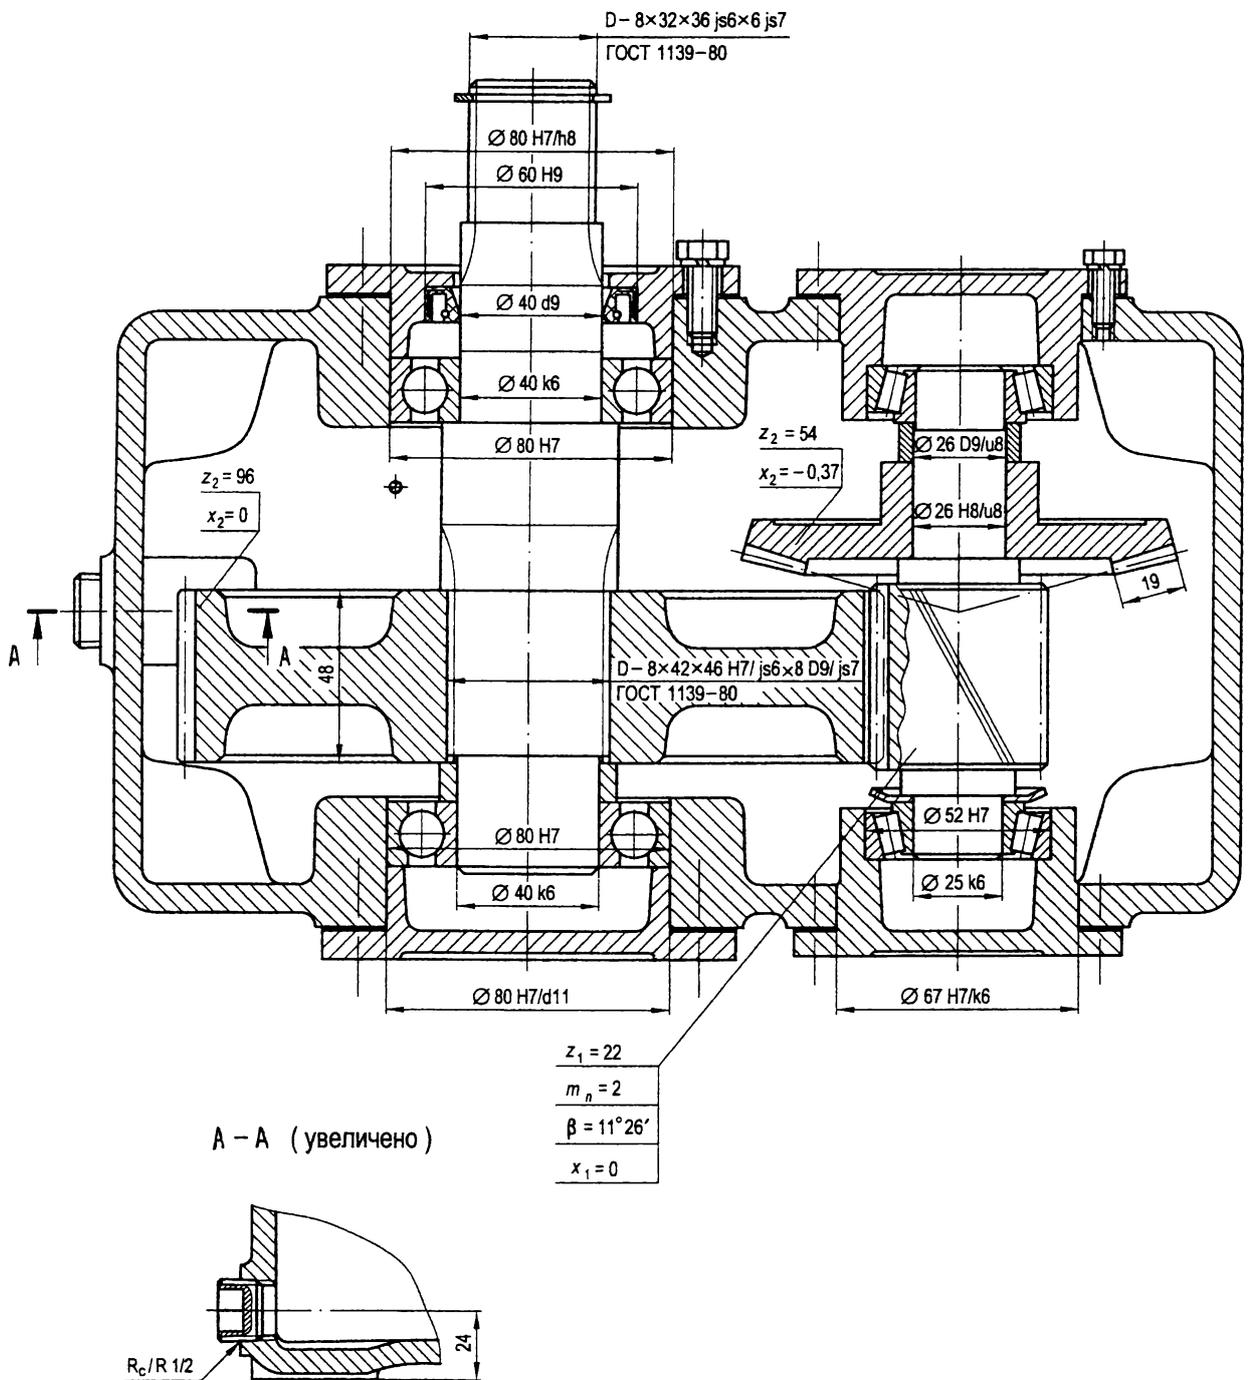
Редуктор двухступенчатый коническо – цилиндрический горизонтальный с вертикально расположенным быстроходным валом конической шестерни, выполненный без разъема корпуса по осям валов
